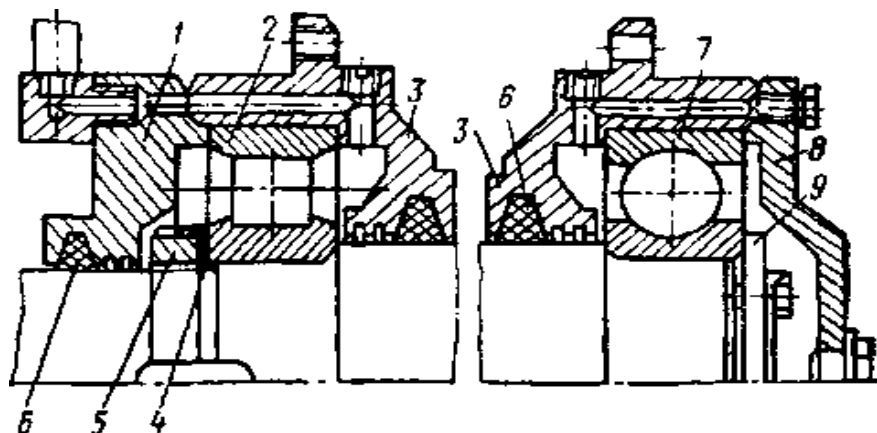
Подшипниковые узлы двигателя компрессора
